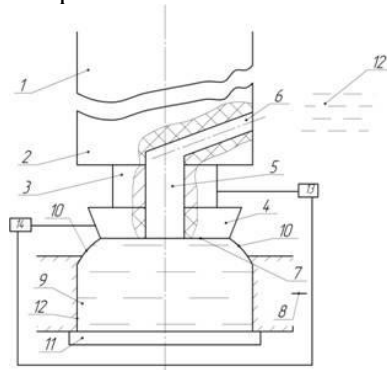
Схема формирования скругления на кромках детали: 1 – электрод – инструмент (ЭИ); 2 – корпус ЭИ; 3 – рабочая часть ЭИ; 4 – направляющая с заборным конусом; 5, 9 – каналы для подачи электролита; 6 – обратный клапан на магистрали подачи электролита; 8 – деталь с рабочим торцом 7; 10 – заусенцы на кромке детали; 11 – заглушка для устранения утечек электролита; 12, 13 – привод для осуществления возвратно-поступательного движения ЭИ 1; 14 – датчик сопротивления движению ЭИ
